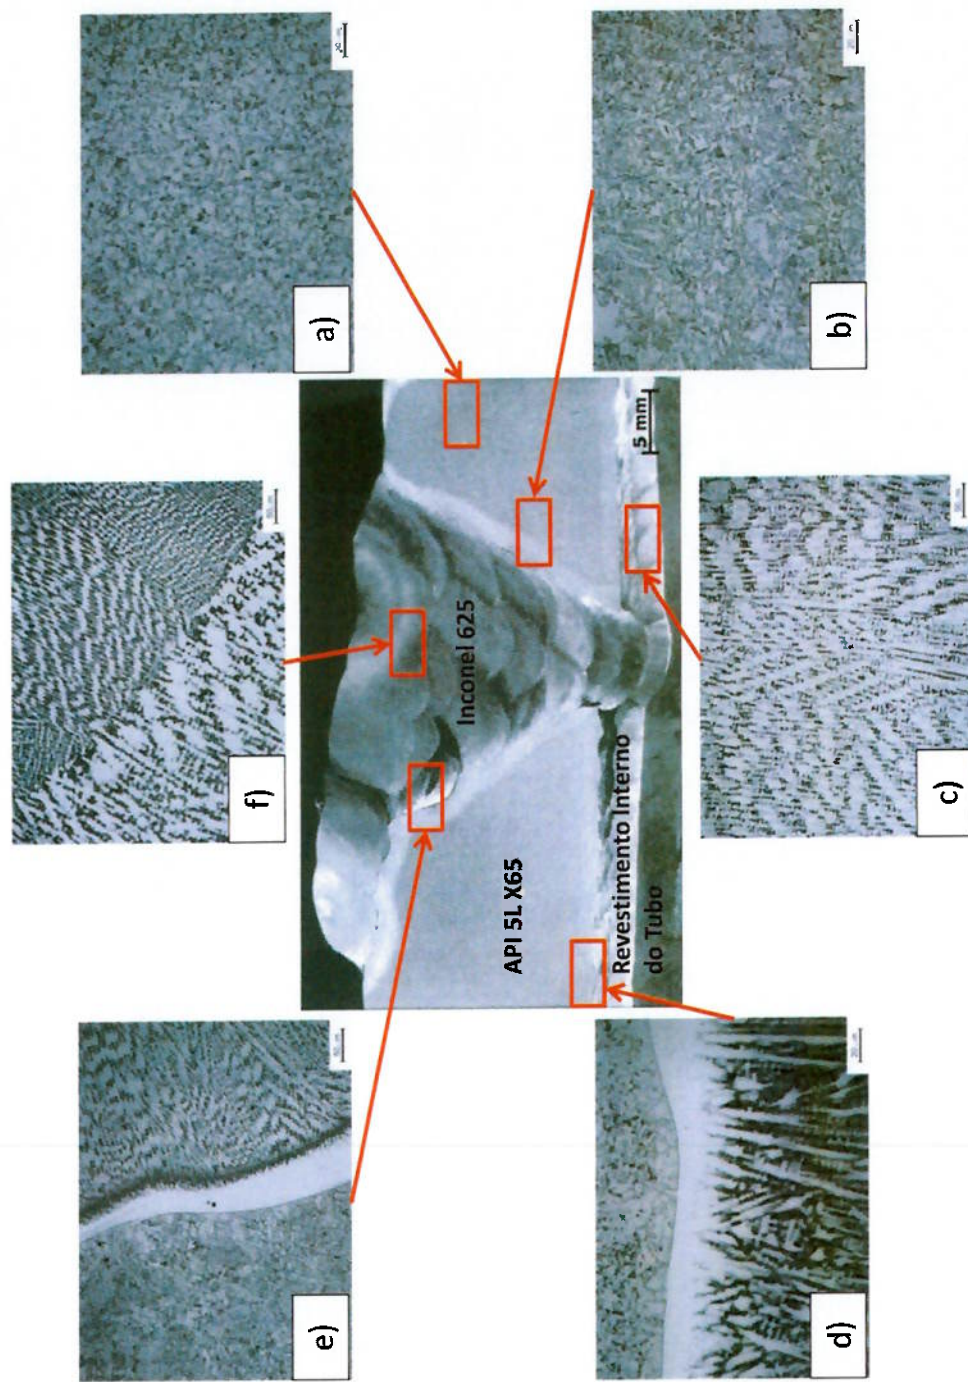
Montagem da macrografia da junta soldada mostrando: a) o metal de base do tubo API 5L X65; b) a ZAC do tubo API 5L X65 causada pela soldagem circunferencial; c) o metal de solda do revestimento interno do tubo API 5L X65; d) a região de transição entre o revestimento interno e o metal do tubo; e) a região de transição entre a ZAC do tubo e o metal de solda da soldagem circunferencial; f) metal de solda da soldagem circunferencial.
